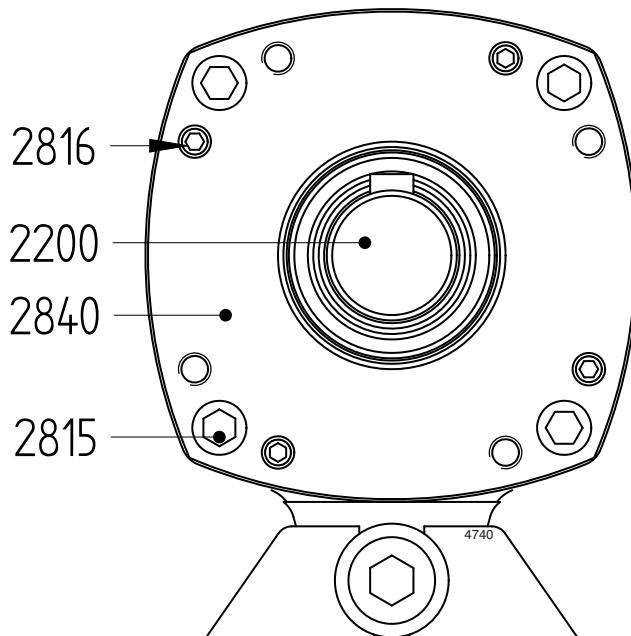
Осевая регулировка конструкции подшипника L5 и L6
